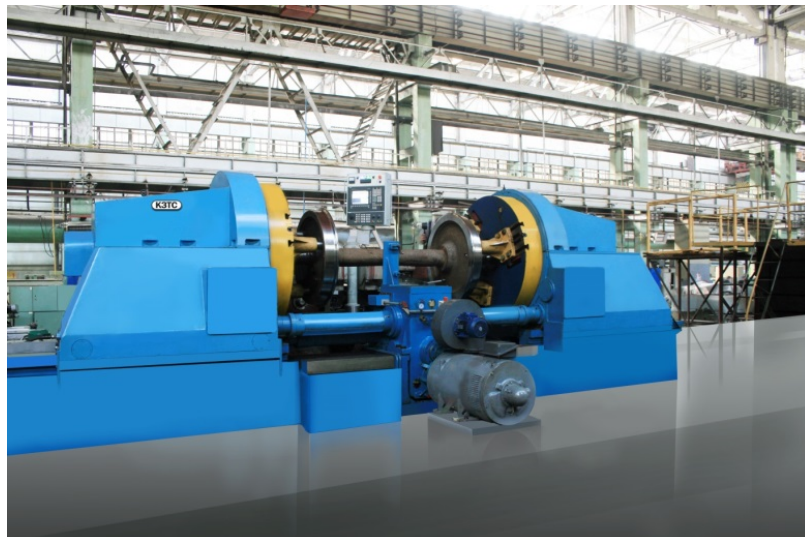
Общий вид колесотокарного станка мод. КЖ 1836М.10
